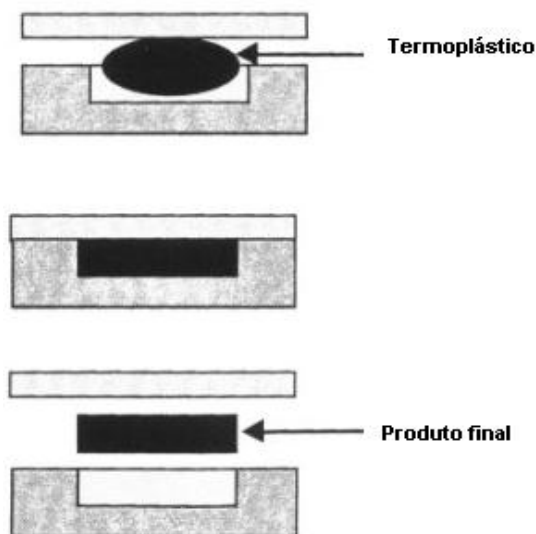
Esquema do processo de moldagem por compressão. Fonte: <http://www.parafusoautovedante.com.br/CapasDeSilicone/MoldagemDeCompressao.asp>
